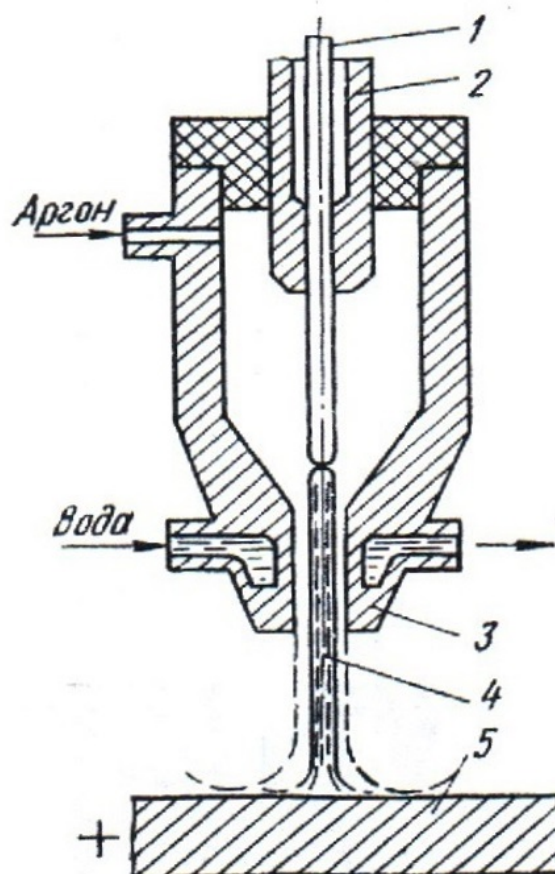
Схема плазменной сварки на прямой полярности:
